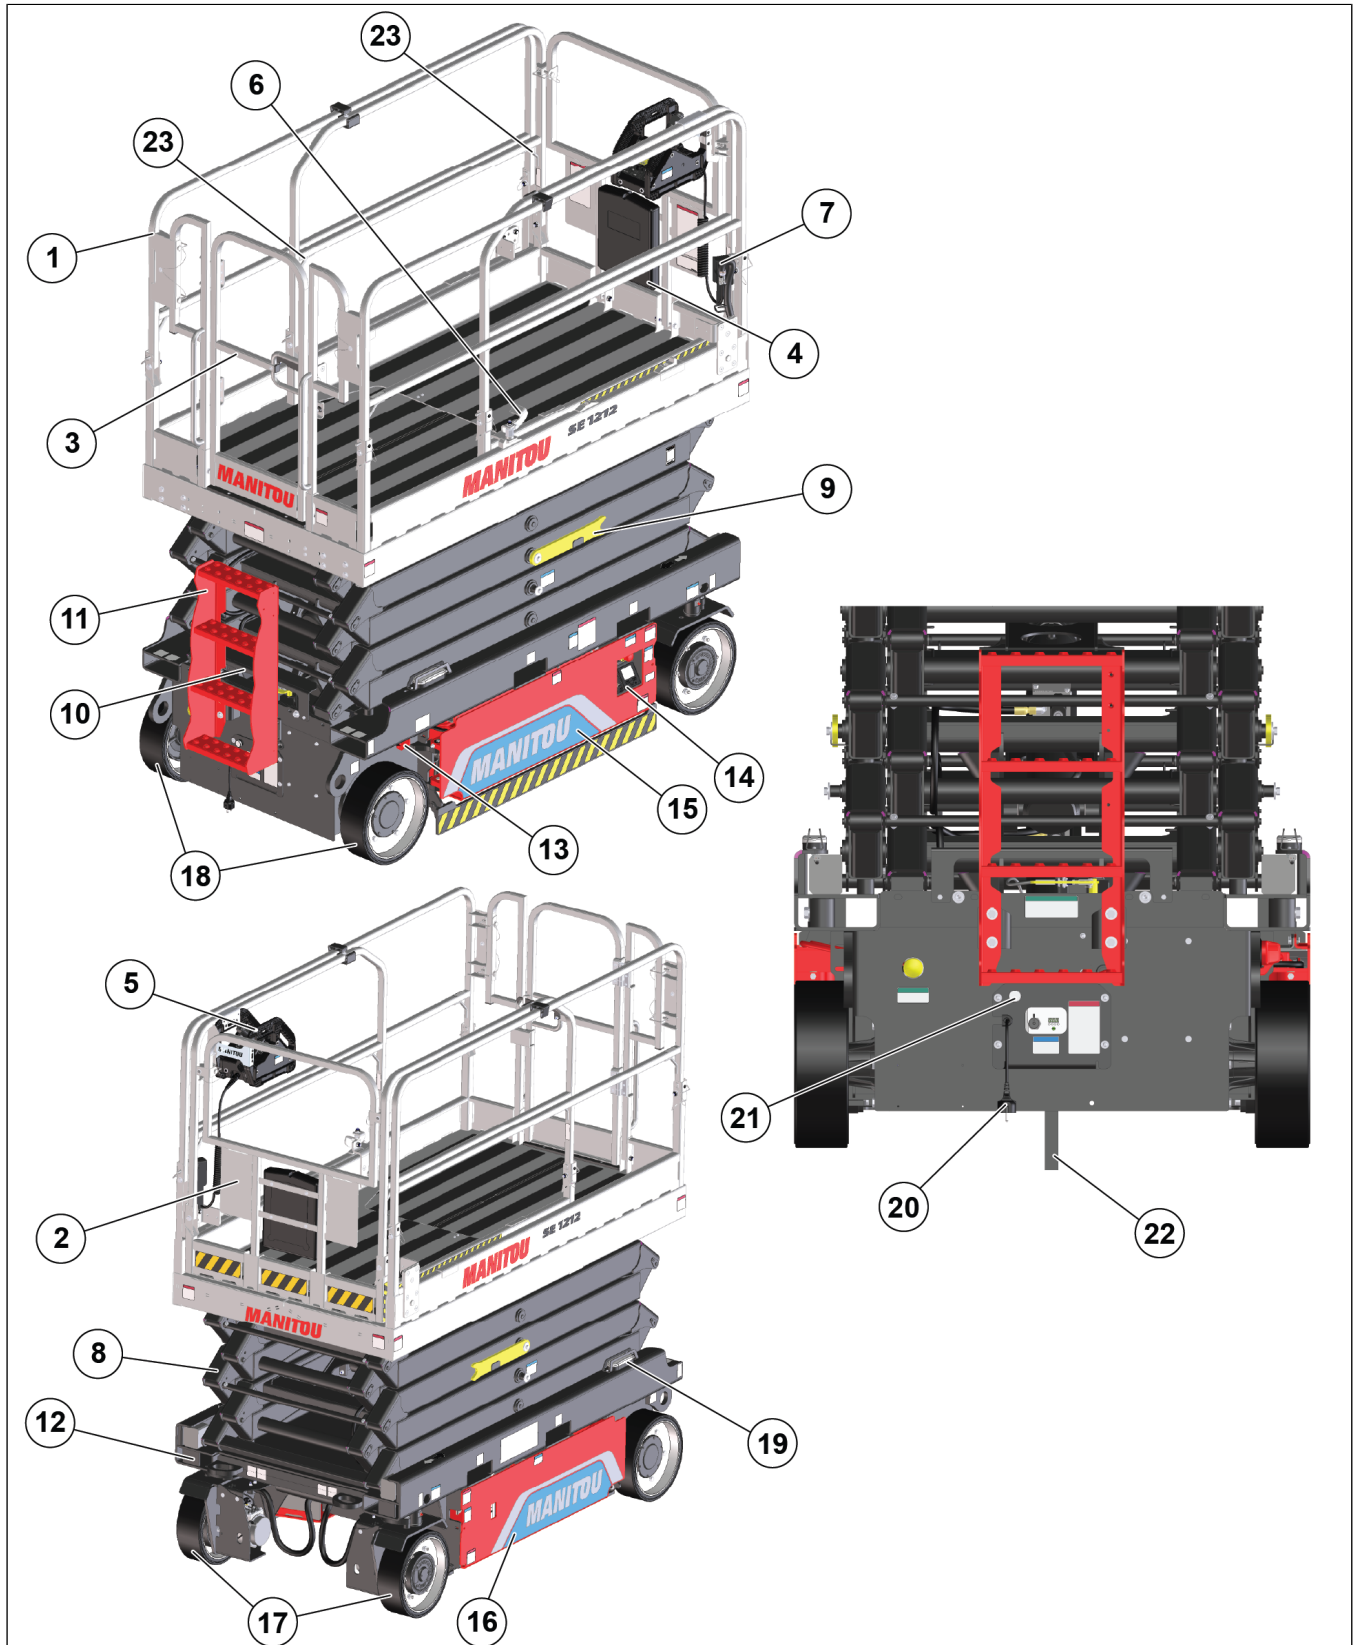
Emplacement des composants de la machine - SE 1212 24V S1
